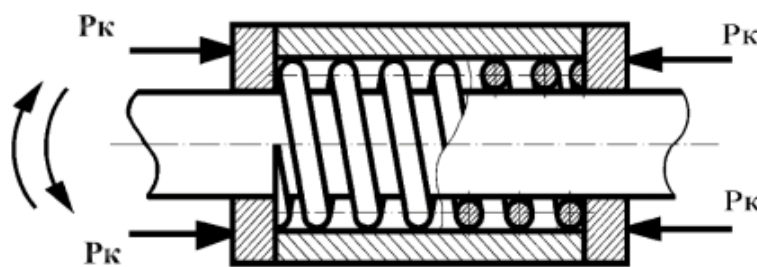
Принципова конструктивна схема підшипника з рухомим пружинним вкладишем
